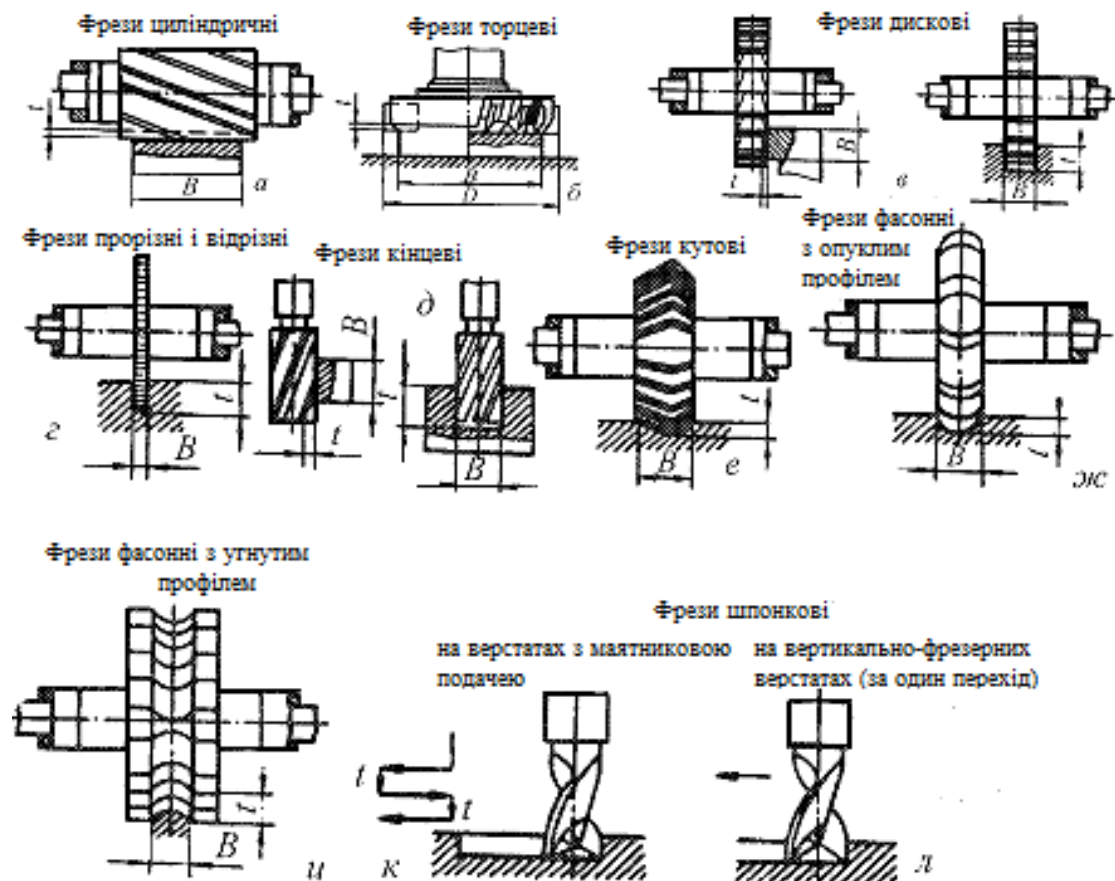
Види робіт, виконуваних на фрезерних верстатах, та застосовувані інструменти
